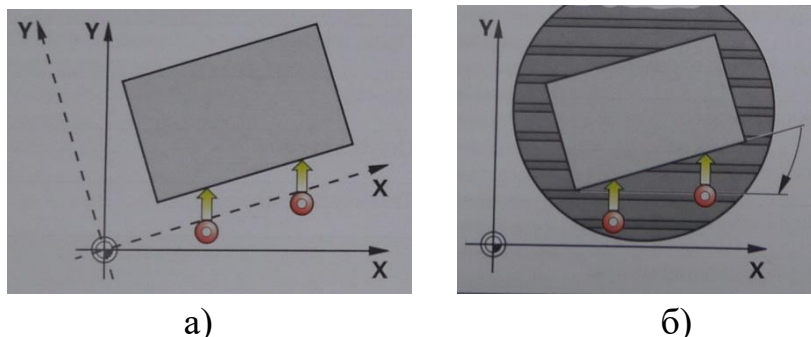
Компенсація відхилення заготовки від напрямку координатних осей: а – обертанням координатних осей; б – обертанням поворотного столу
